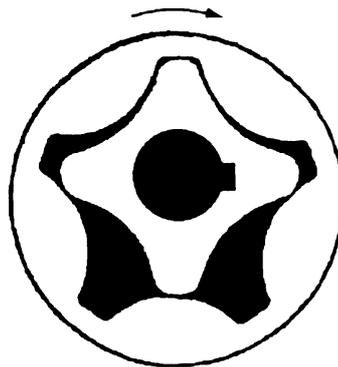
Bomba de engrenagens internas tipo gerotor (LINSINGEN, 2001)
